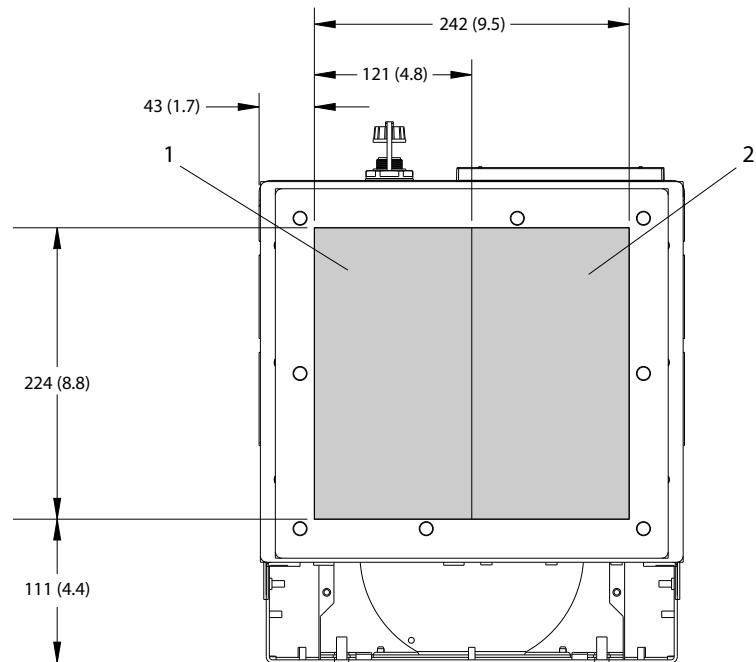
Dimensi Akses Heat Sink untuk D5h
